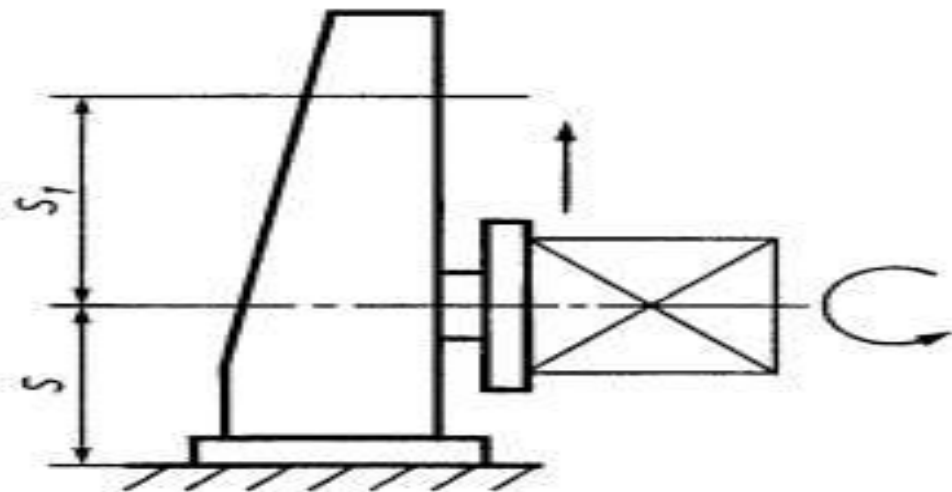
Кантователь центровой с подъемными центрами
